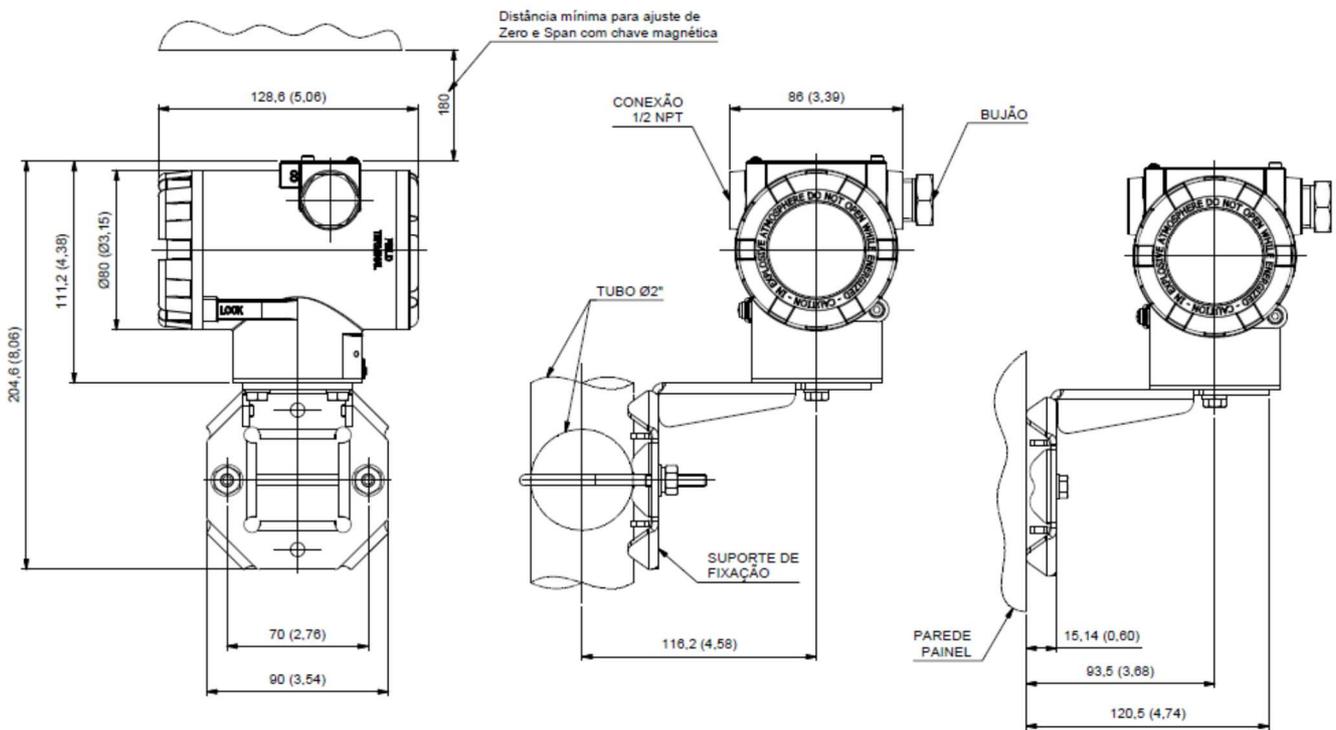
Desenho dimensional e formas de montagem do VRI10-I.
